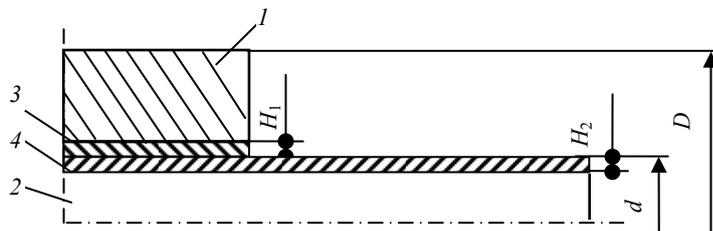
Многослойное прессовое соединение: 1 – охватывающая деталь; 2 – охватываемая деталь, 3 – медное гальваническое покрытие на охватывающей детали; 4 – цинковое гальваническое покрытие на охватываемой детали
